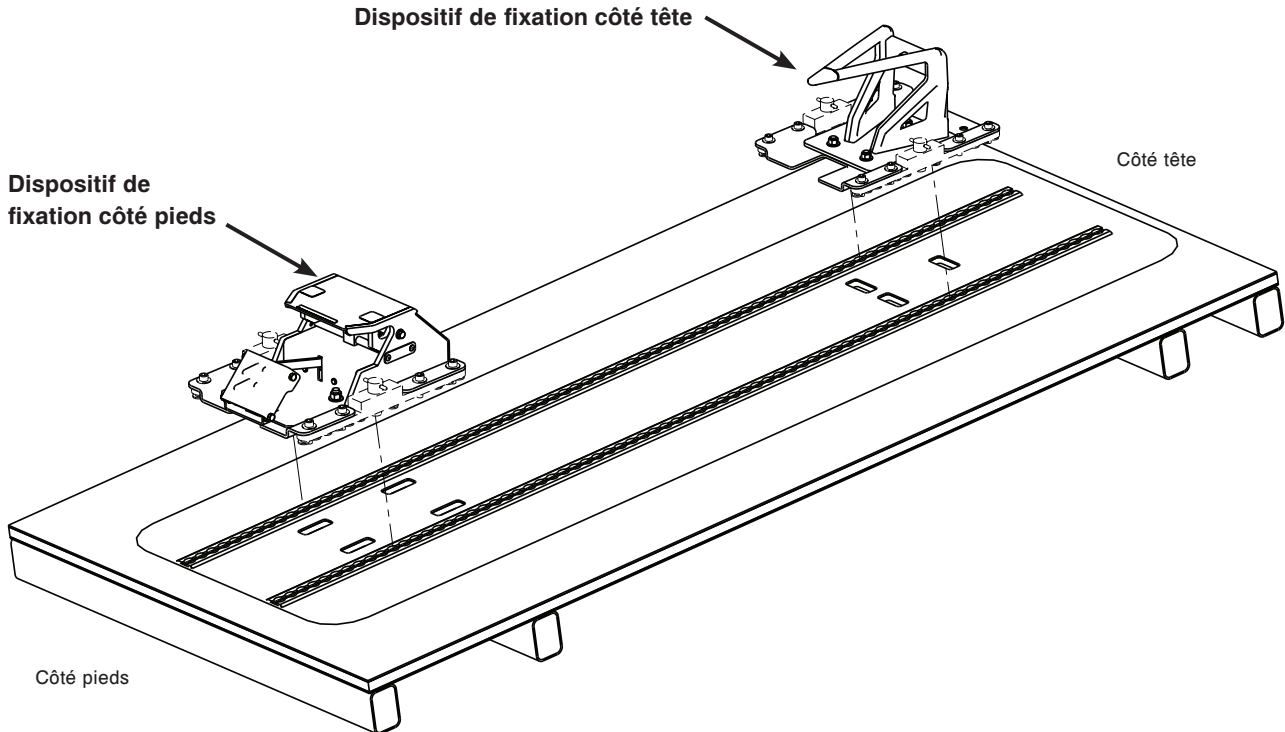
Dispositif de fixation côté tête et côté pieds – installation des rails de plancher
